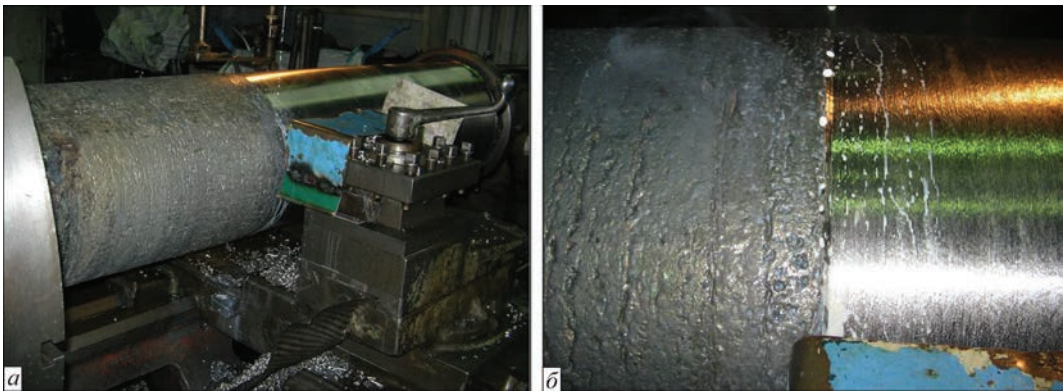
Механічна обробка зливка діаметром 400 мм жароміцного ХН60ВТ
